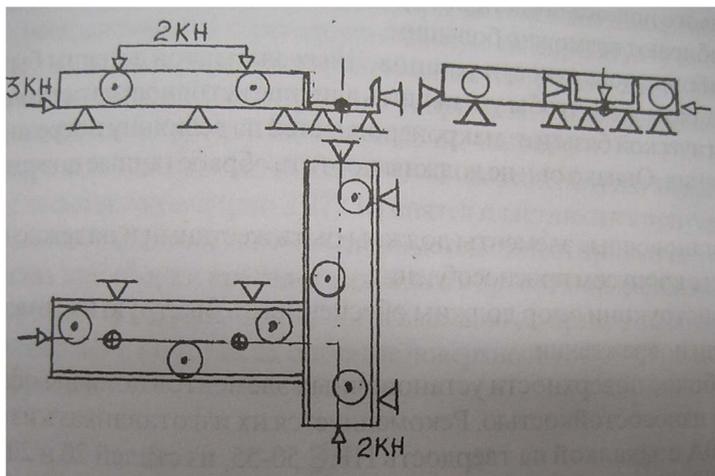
Пример принципиальной схемы базирования приспособления для сборки
